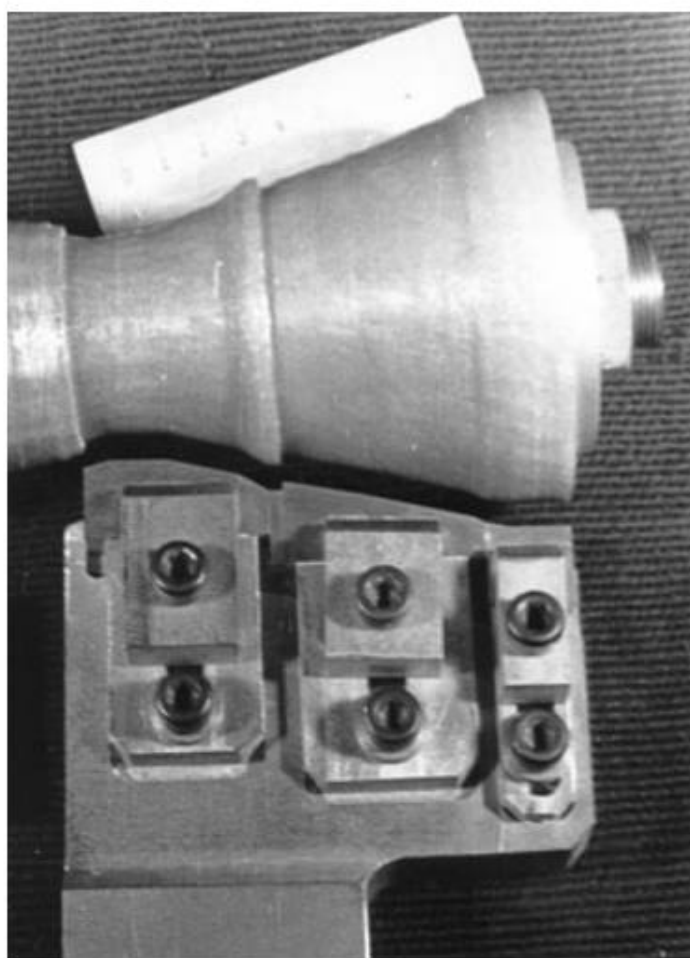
Резцовый блок для изготовления наружной поверхности раструба корпусного изделия с применением МШС
